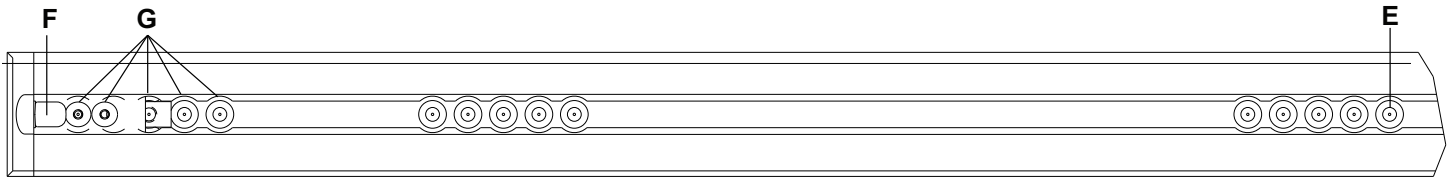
Posición del posicionador de la placa de suelo - extremo de los pies
